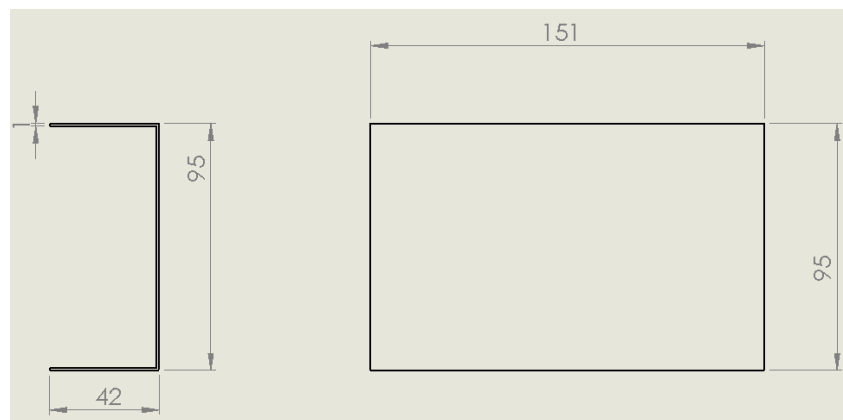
Sensor LVDT: a) Pieza componente; b) Dimensiones. Fuente: Autor.
